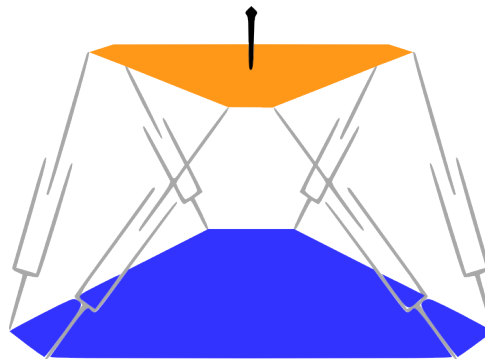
Hexapod bestehend aus Basis, 6 Teleskopbeinen und Plattform sowie einem Werkzeug mittig auf der Plattform
